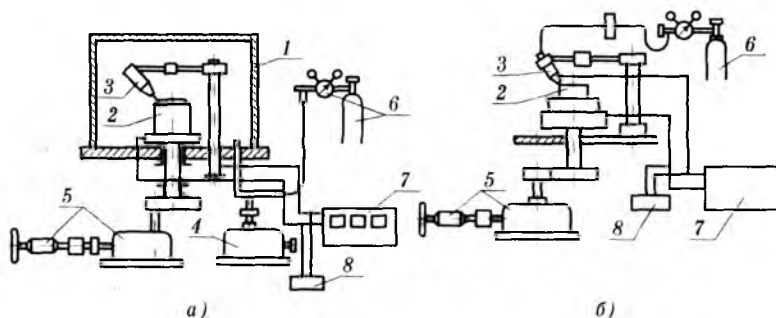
Схема установки для аргонодуговой сварки в закрытой камере (а) и с обдуванием дуги аргоном на воздухе (б):
